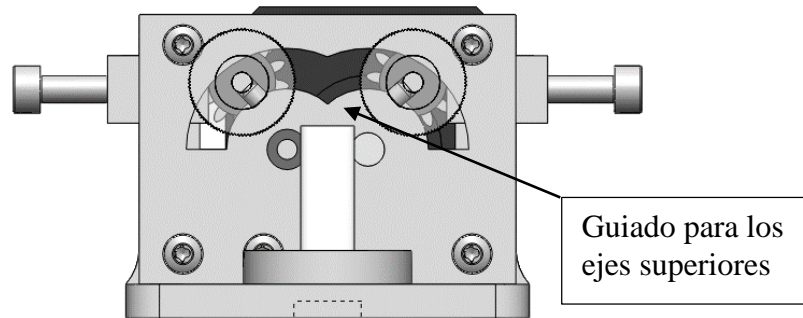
Sistema de guiado del extrusión de engranajes pivotantes (Versión 01)
